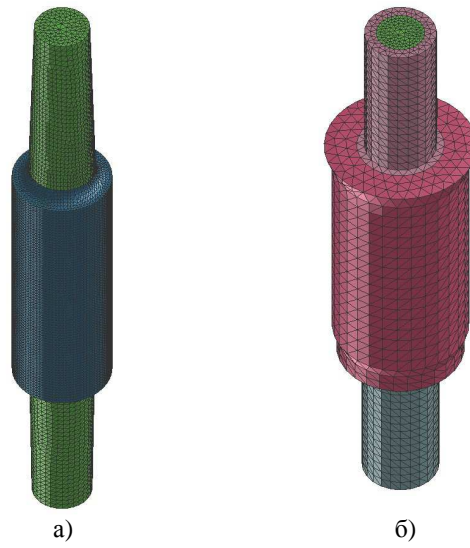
Расчетные 3D-модели валковой отливки (а) и формы
